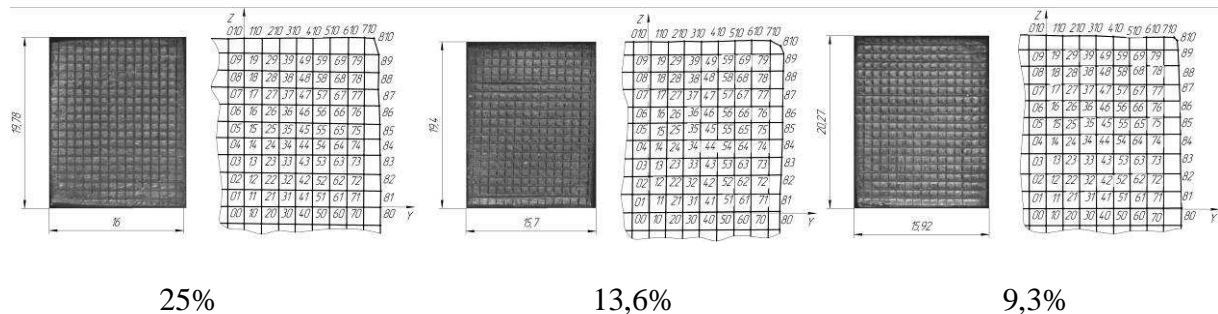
Загальний вигляд поперечного перерізу вихідних заготовок
